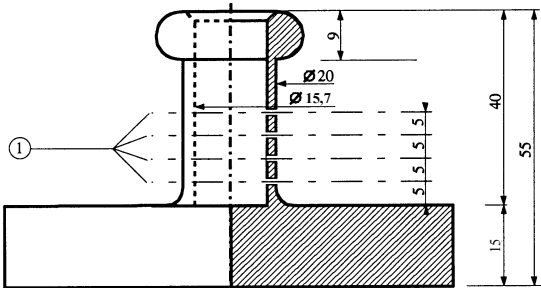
Полый бронзовый цилиндр, закрытый с одной стороны; чертеж и размеры детали в мм
